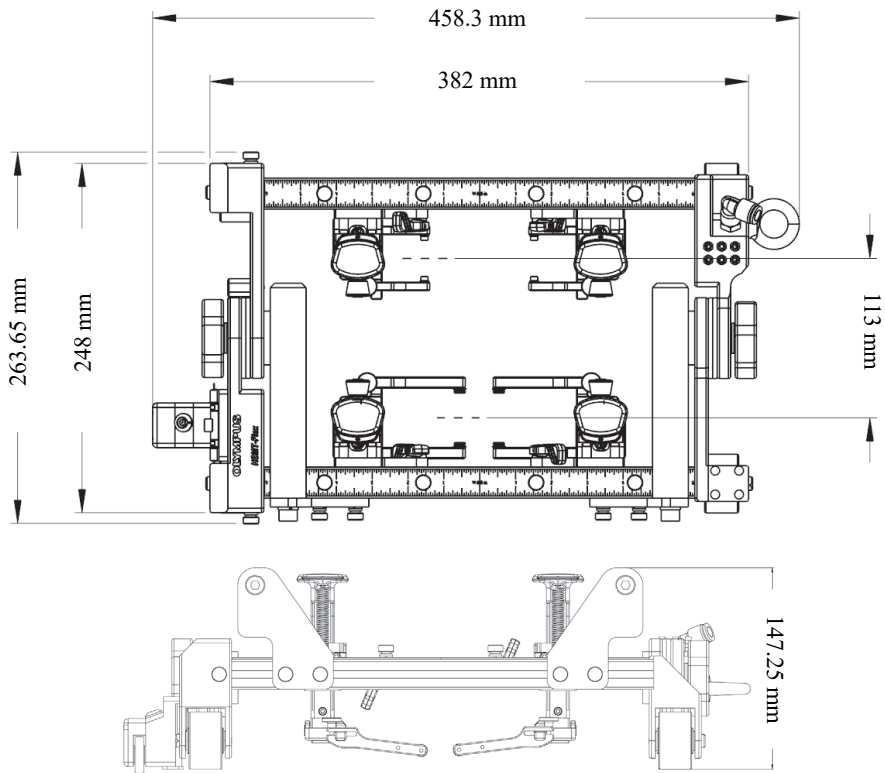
扫查器的尺寸 — 俯视图和侧视图
